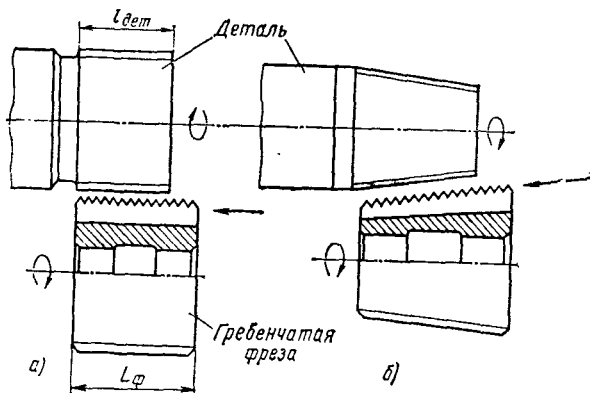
Схема фрезерования резьбы многониточными (гребенчатыми) резьбовыми фрезами:
